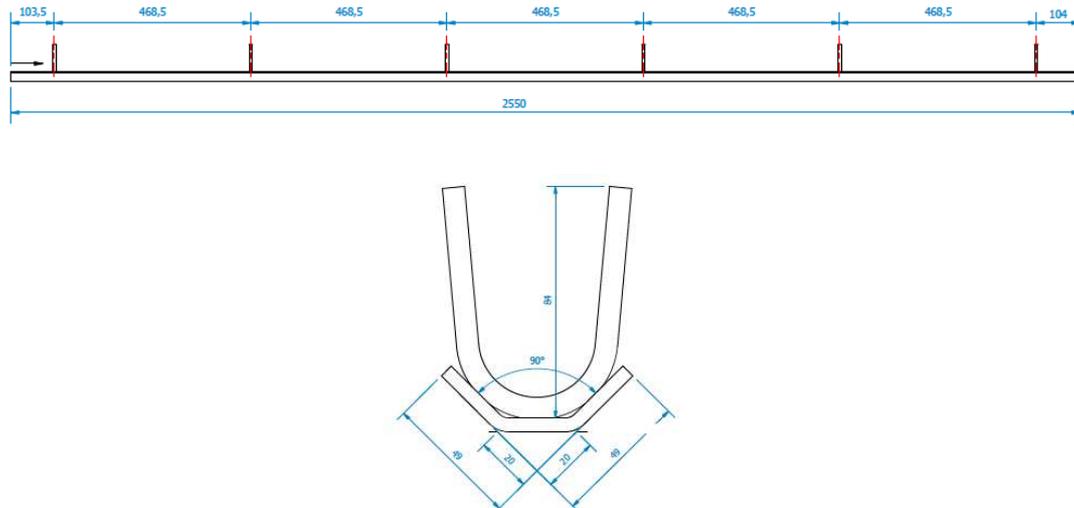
Dimensiones longitudinales y seccionales de las cantoneras PROXI
